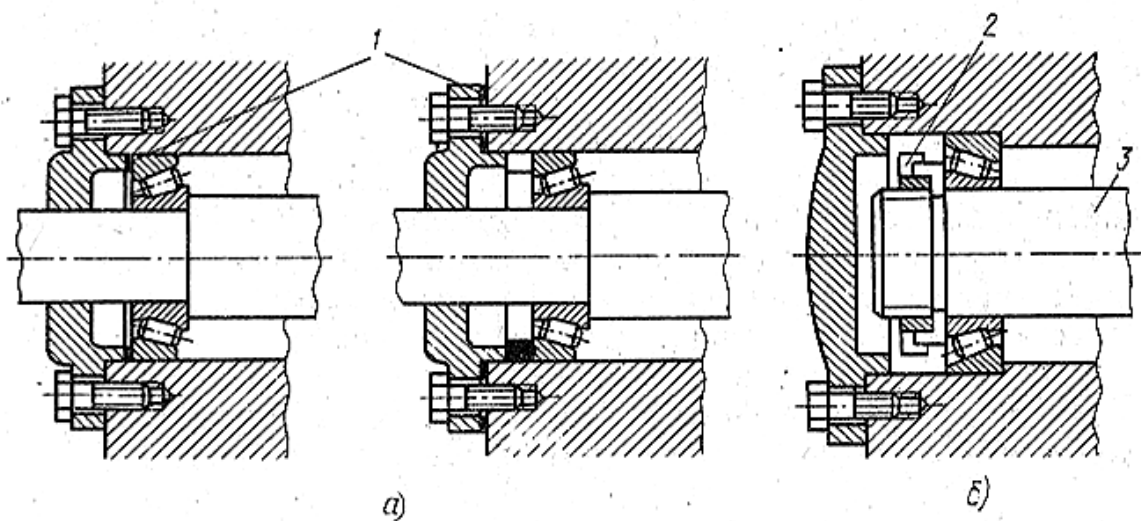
Регулировка зазора у конических и роликовых подшипников с помощью регулировочных прокладок (а) и регулировочной гайки (б):
